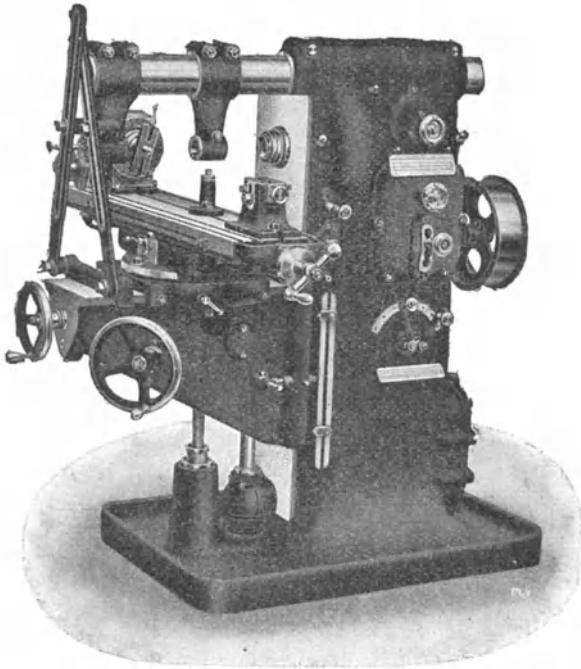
Die Universalfräsmaschine der Wanderer-Werke.
